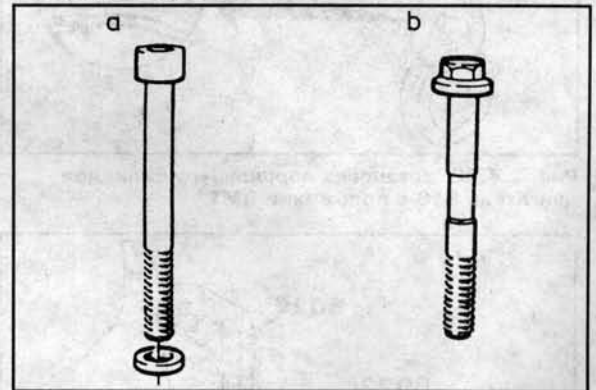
Два типа болтов головки: старый (а) и новый (б)
